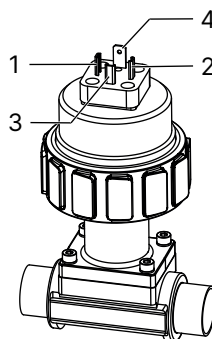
Anschlussbelegung der Hall Low Power-Variante
